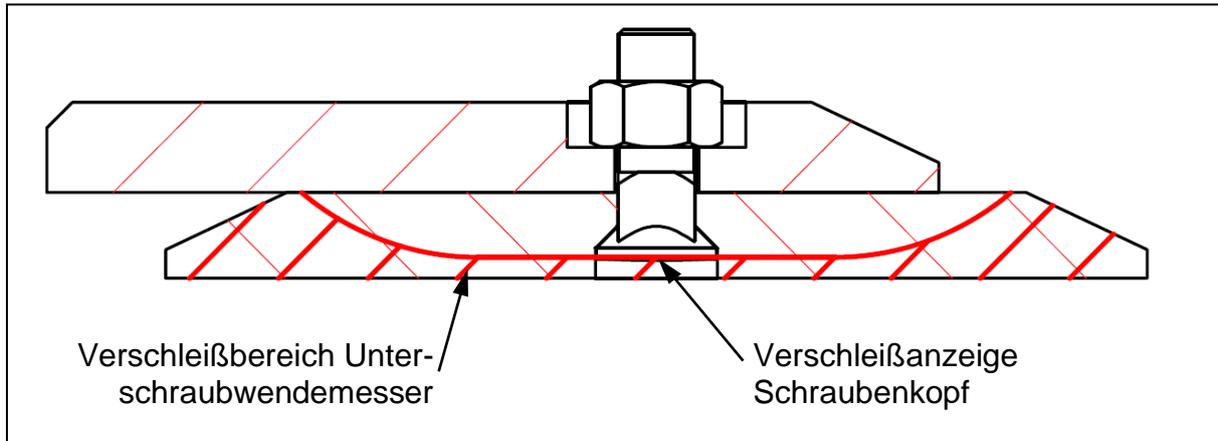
Verschleißzustand Unterschraubwendemesser
